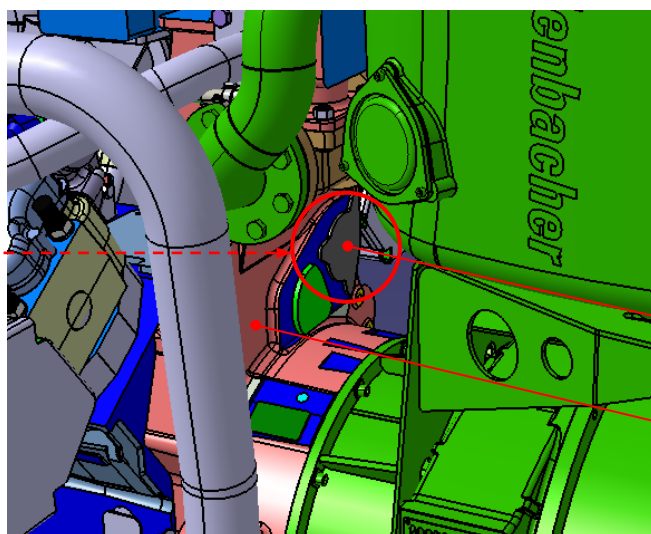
Zeichnung - Kühlwasserleitung für elektrische Motorkühlwasserpumpe (1)
